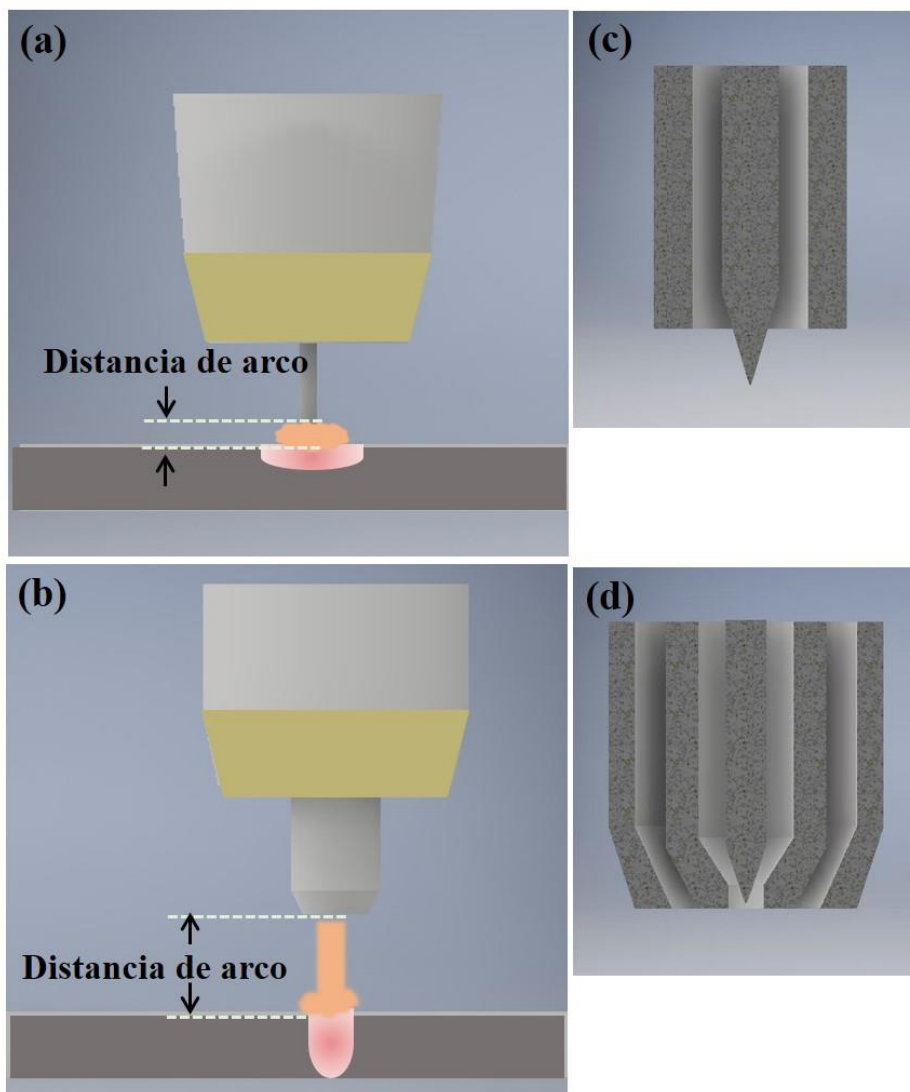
Esquema representativo del diseño de boquilla que utiliza: (a), (c) el proceso GTAW y (b), (d) proceso PAW, imagen adaptada de [17].
